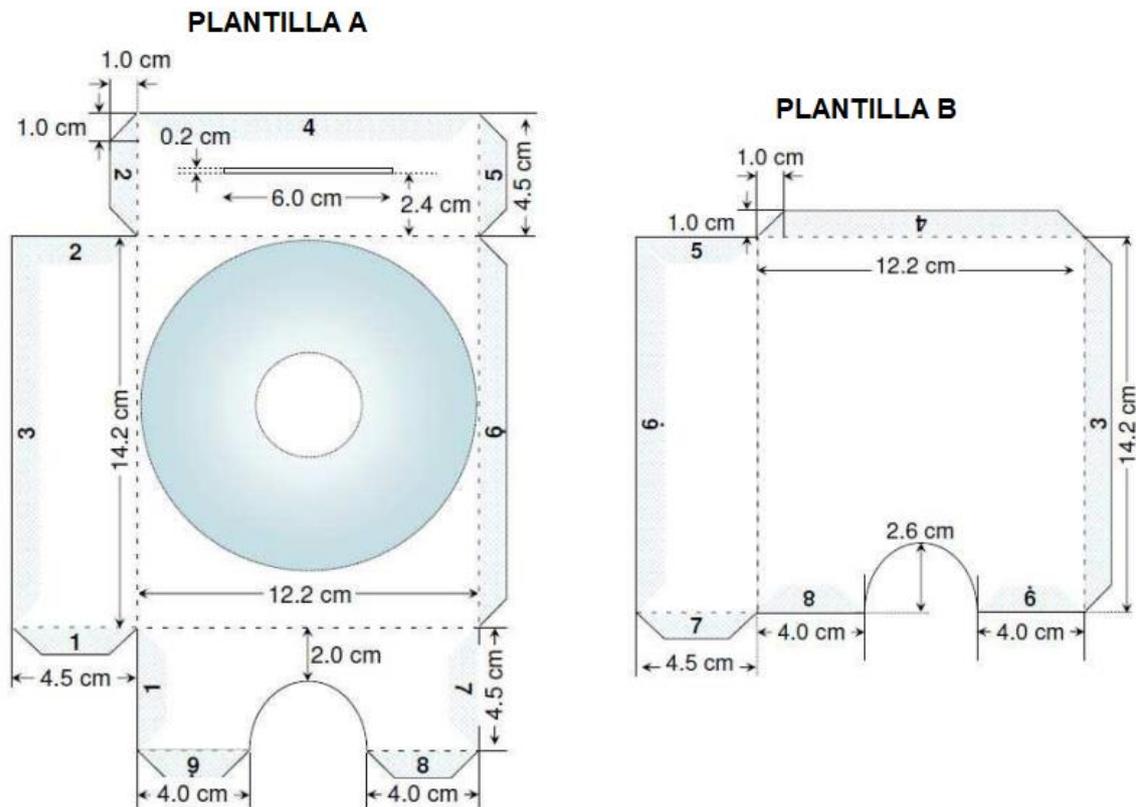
Plantillas A y B. Santolaya, (2009).
